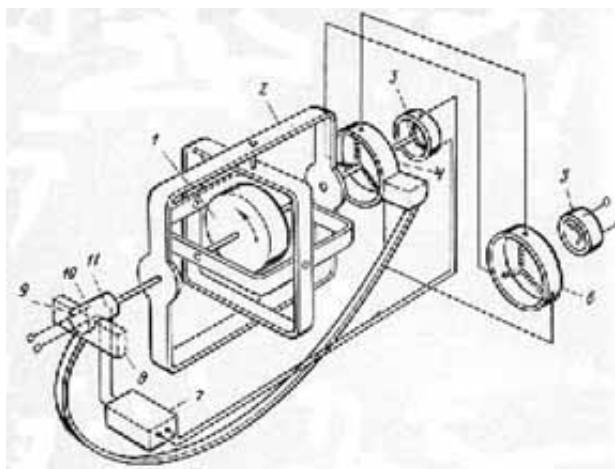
Кинематическая схема гироагрегата курсовой системы.
